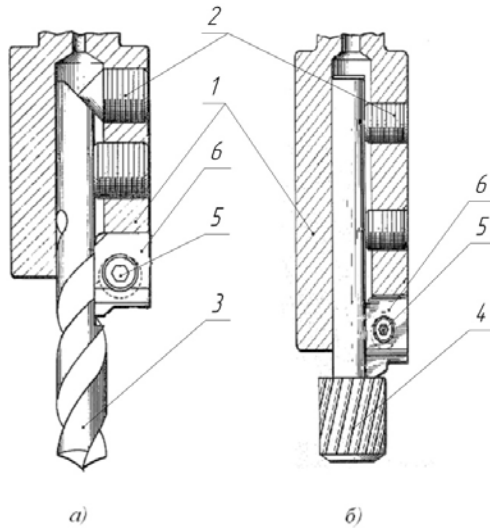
Збірний КОІ компанії Everede Tool Company у виконанні: а – свердло-зенківка; б – розвертка-зенківка
